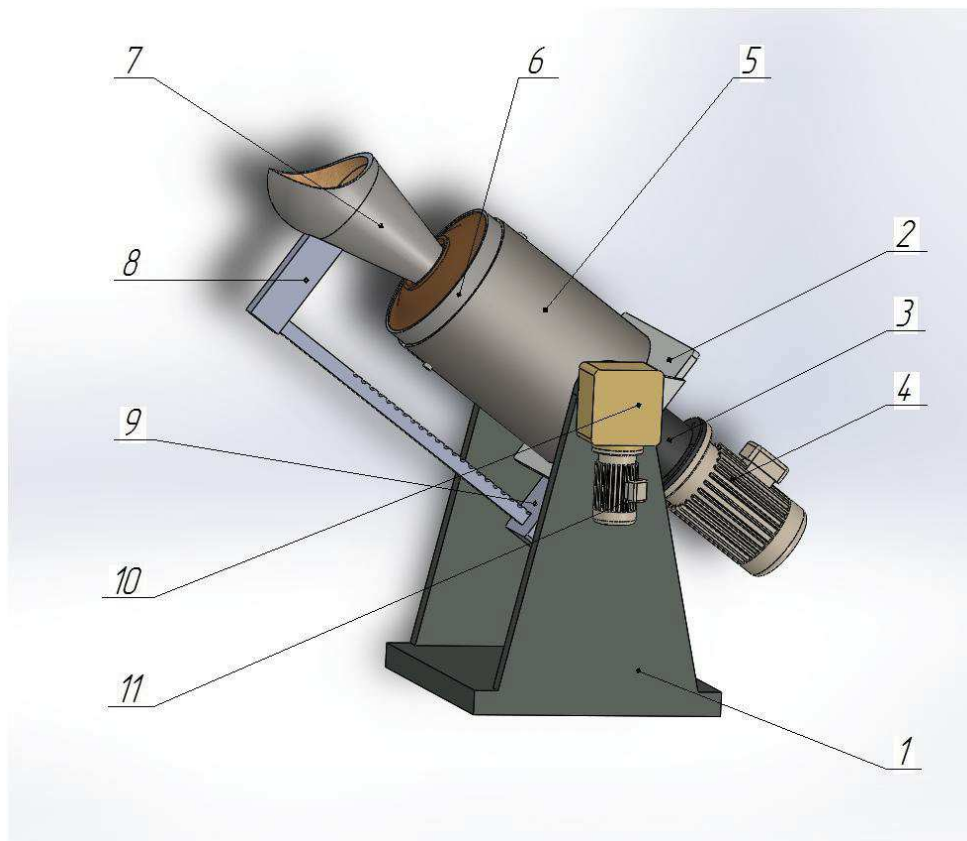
Конструкція установки відцентрового литва та армування заготовок
